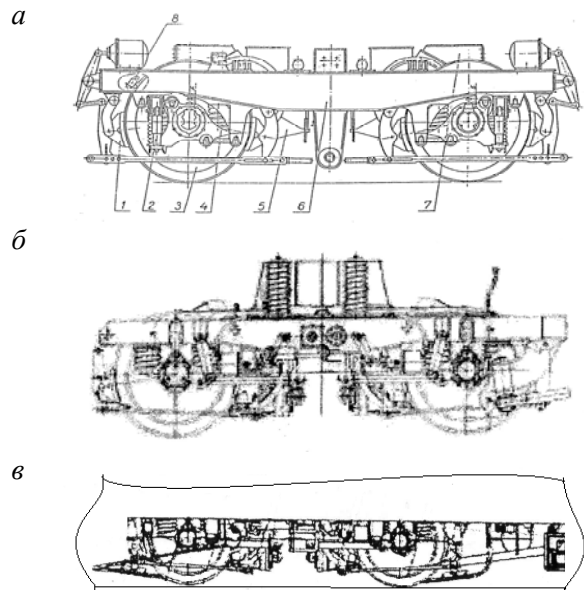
Схемы тележек электровозов серий ЭП10 (а); 2ЭС6 «Синара» (б); 2ЭС10 «Гранит» (в): 1 – тормозная система, 2 – установка гидродемпферов, 3 – колесная пара с буксами и редуктором, 4 – рессорная система буксовой ступени, 5 – корпус тягового редуктора, 6 – рама тележки, 7 – тяговый двигатель, 8 – устройство смазки гребней
